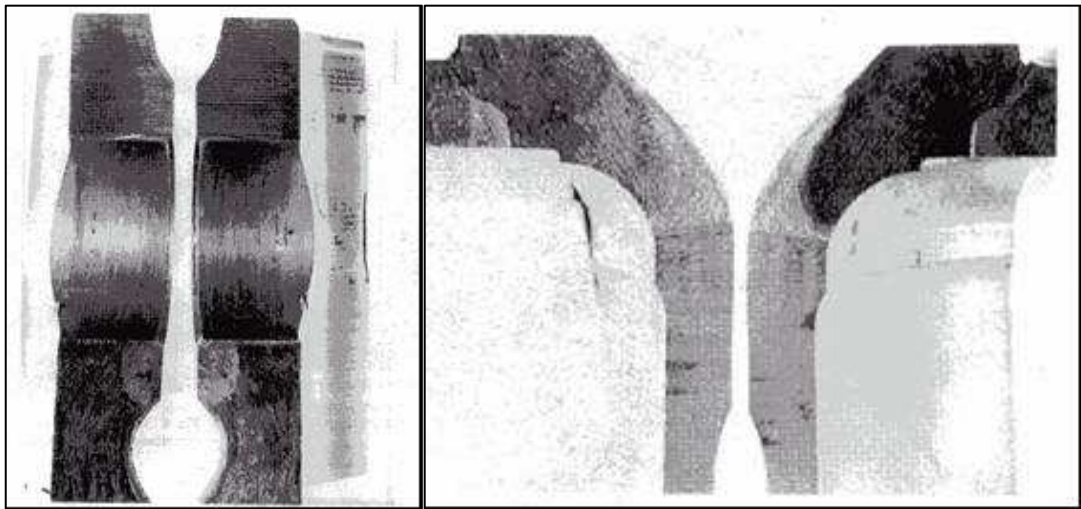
Grieta abierta en parte 5 y daño mecánico en parte 3.
